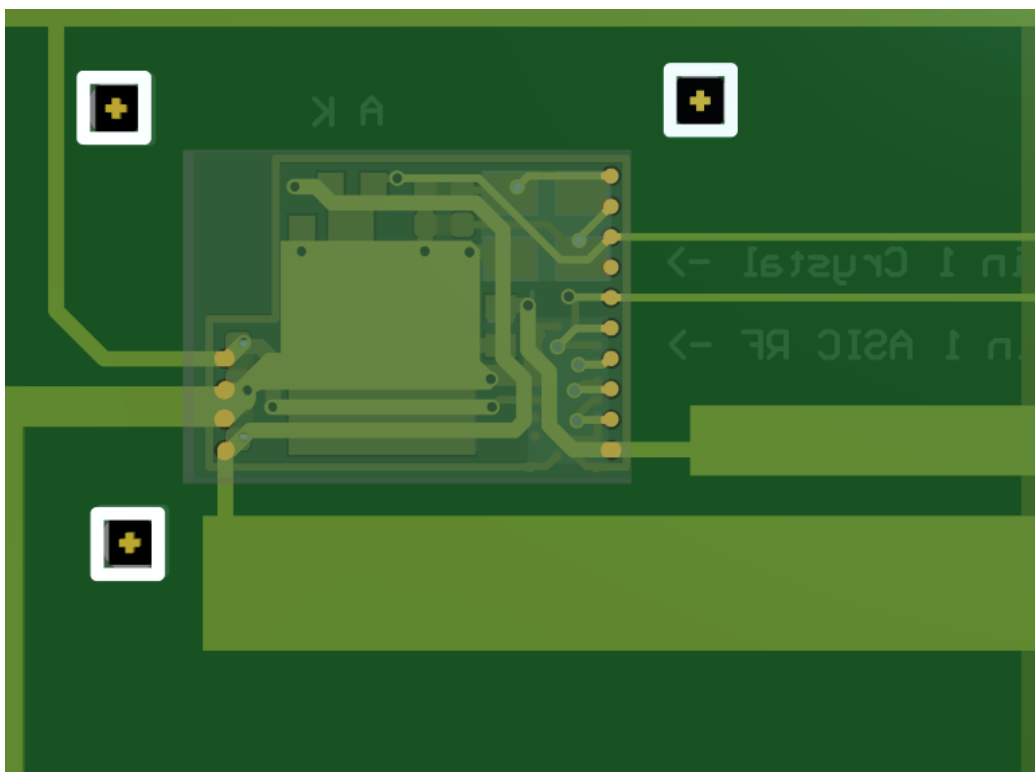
Image agrandie sur les *pads* de la face de dessous du PCB interposeur
